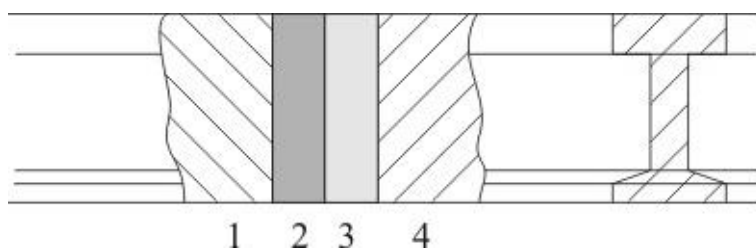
Схема сварного соединения: 1 – рельс Э76; 2 – вставка сталь 20; 3 – вставка 12X18H10T; 4 – крестовина 110Г13Л [10]
